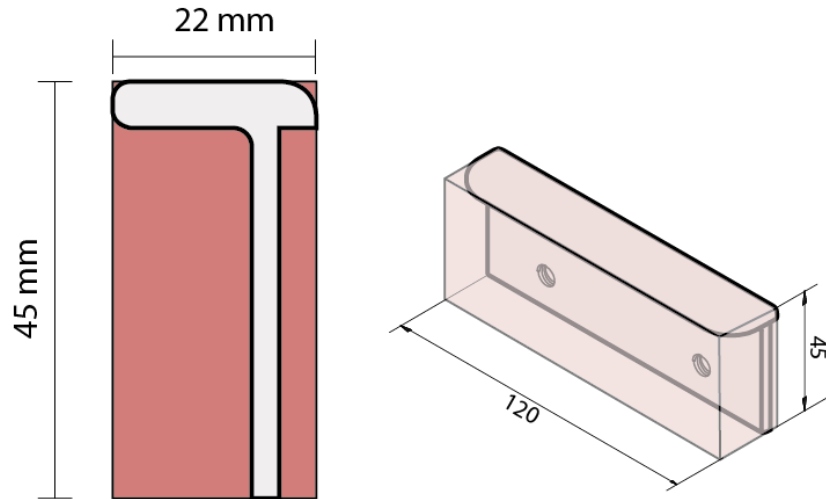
Dimensiones y desbaste de la jaladera para corte en plancha de grilon
